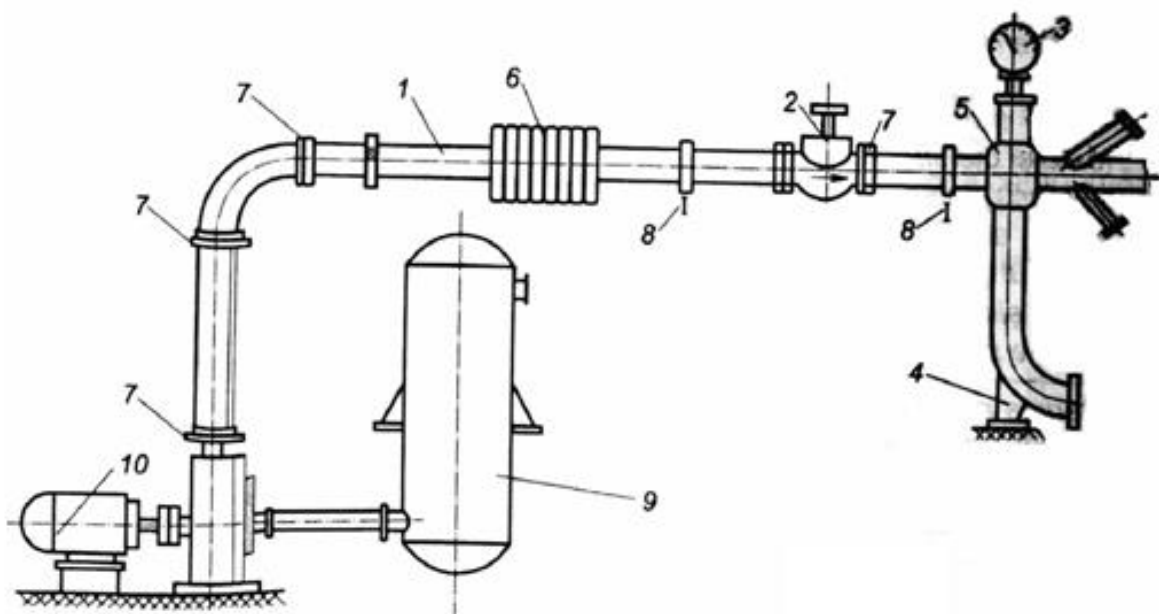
Elementele constructive ale unei instalații de transport a fluidelor.
